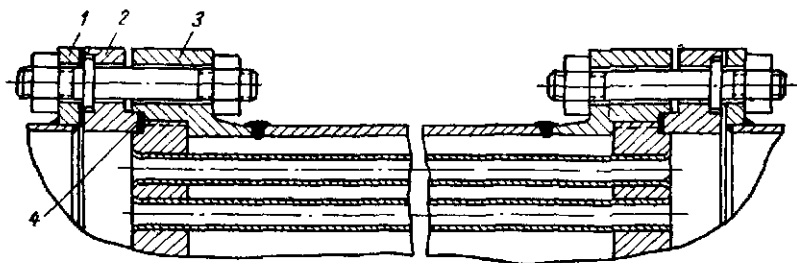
Конструкция крепления трубной доски к фланцу корпуса.
